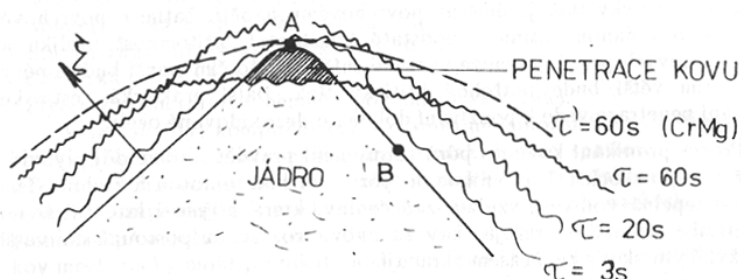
Časový průběh působení mechanismů mechanické penetrace [10]
